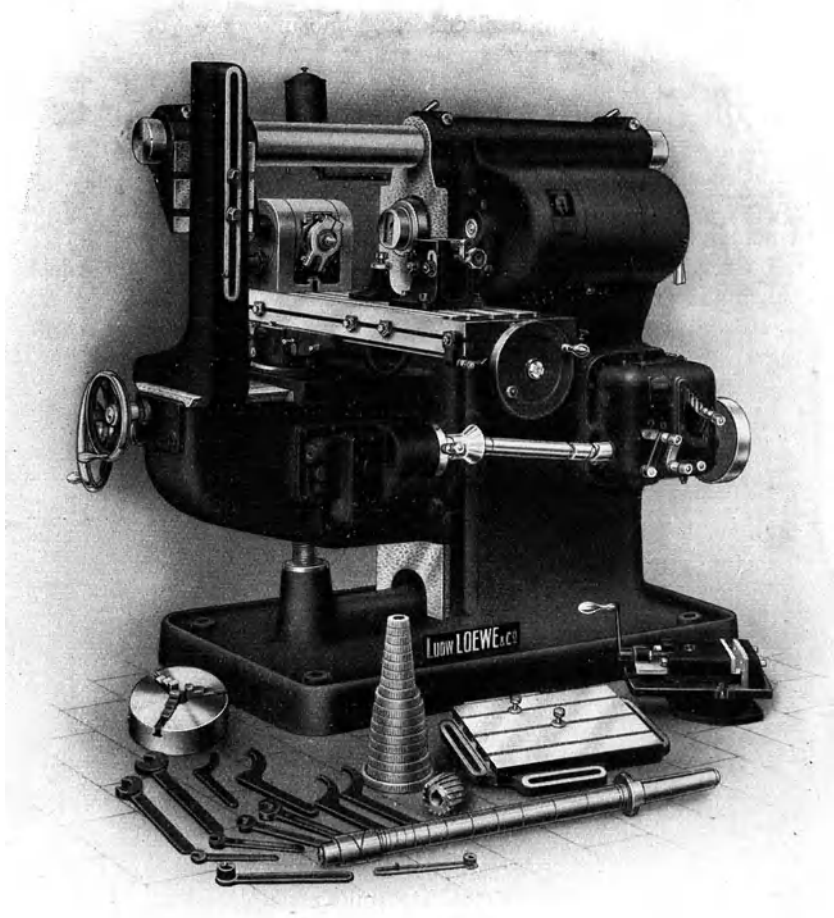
Die Universalfräsmaschine von L. Löwe & Co.
